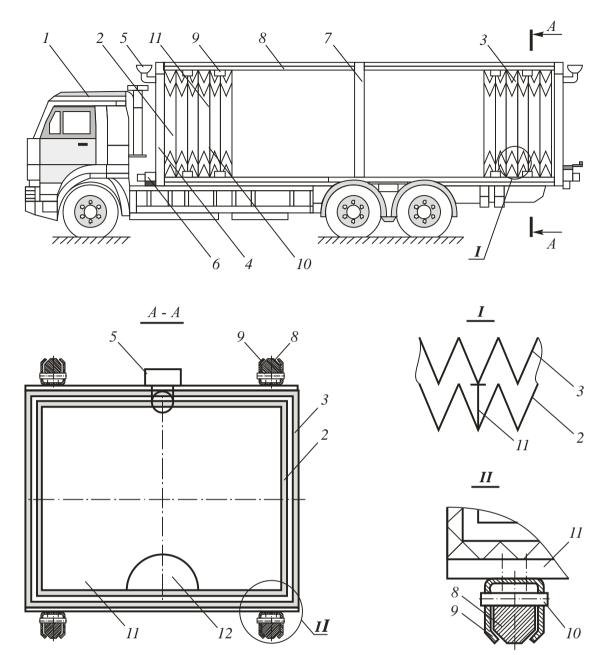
Транспортное средство в сборе: 1 — грузовой автомобиль; 2 — гофрированные резервуары; 3 — защита теплоизоляционная; 4 — баки; 5 — заливные горловины; 6 — сливные краны; 7 — металлическая арка; 8 — направляющая; 9 —держатель; 10 — ролик; 11 — поперечные волнорезы; 12 — отверстия; 13 — ограничители.
